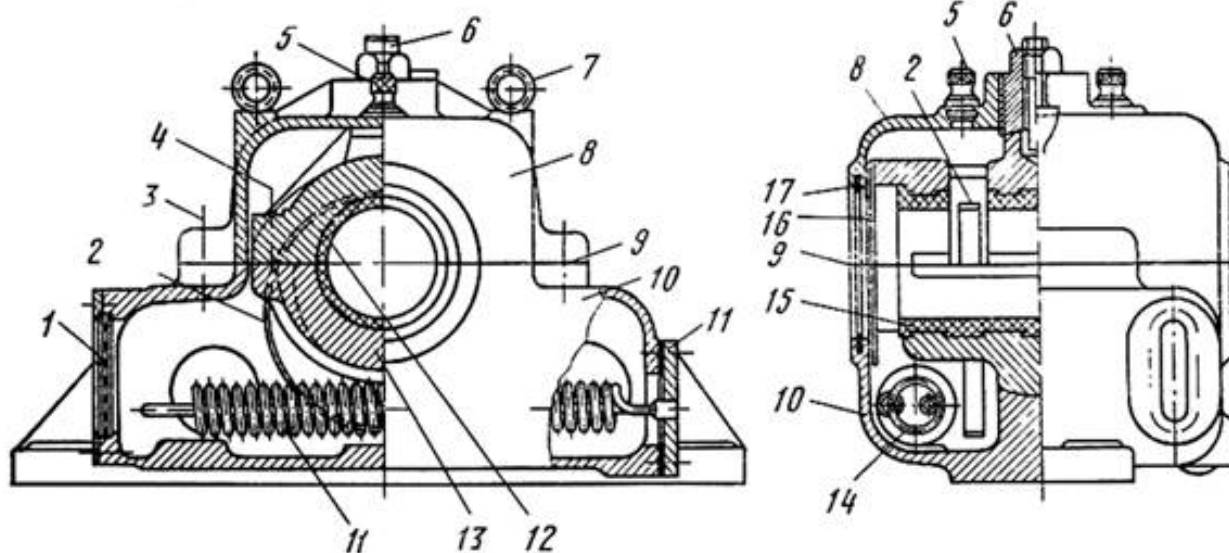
Подшипник дымососа с самоустанавливающимися вкладышами и кольцевой смазкой: 1 – смотровое стекло, 2, 16 – смазочное и маслоотбойное кольца, 3, 4 – шпильки крепления крышки вкладышей, 5, 6 – смотровая и прижимная пробки, 7 – рым, 8, 11 – крышки корпуса и лючка, 9 – линия разъема корпуса подшипника и вкладышей, 10 – корпус, 12, 13 – верхний и нижний вкладыши, 14 – змеевик, 15 – баббитовая заливка, 17 – уплотнение вала
